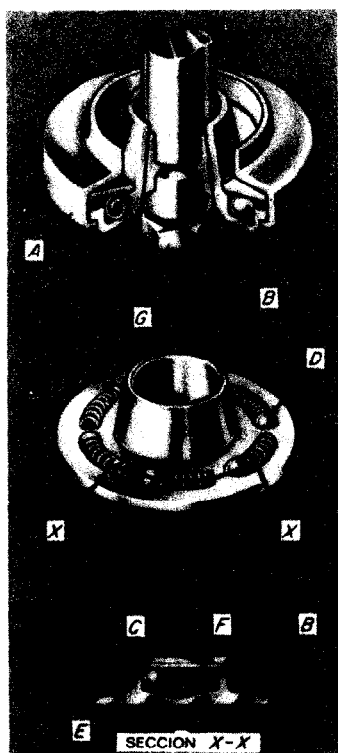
Construcción de un rotador forzado de válvulas: (A) platillo, (B) collar, (C) arandela flexible, (D) bolas, (E) rampa, (F) muelle recuperador, (G) taqué (TRW Inc.).
